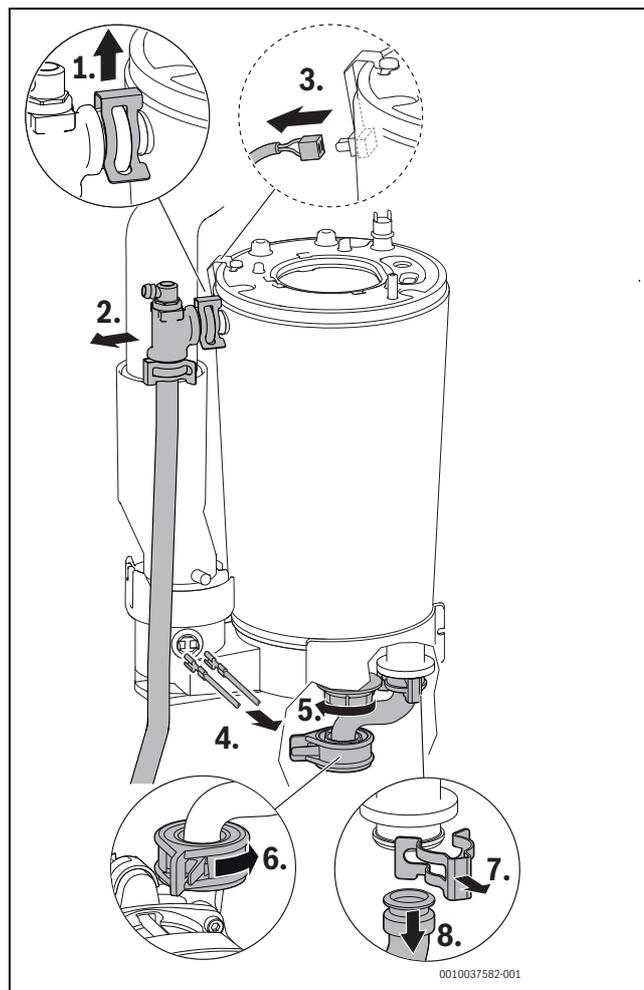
Détacher le tube de départ, retirer le câble et détacher le tube retour
